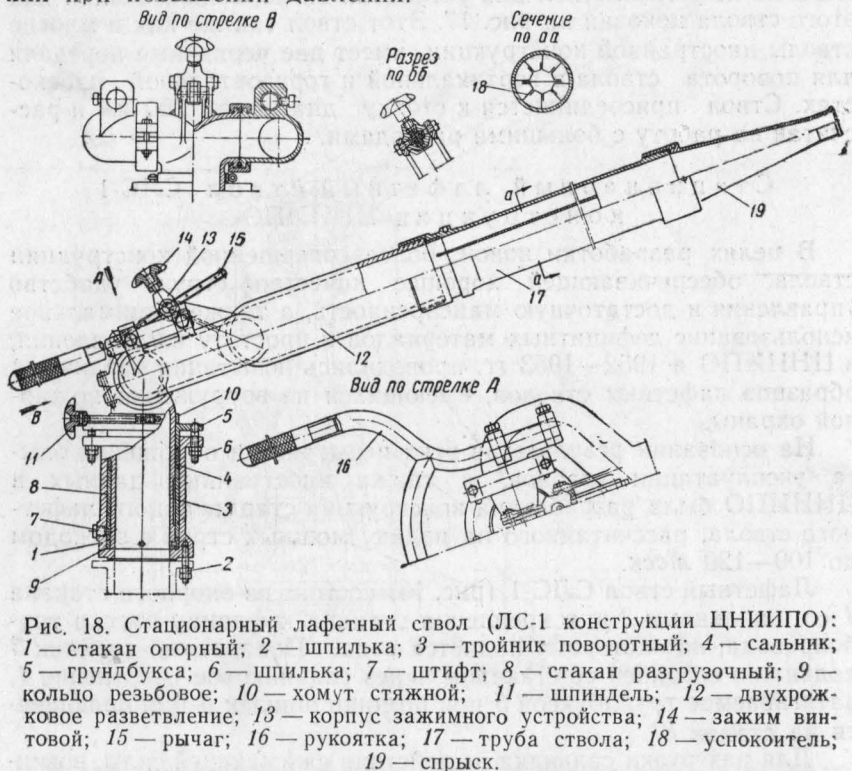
Стационарный лафетный ствол (ЛС-1 конструкции ЦНИИПО): 1 — стакан опорный; 2 — шпилька; 3 — тройник поворотный; 4 — сальник; 5 — грундбукса; 6 — шпилька; 7 — штифт; 8 — стакан разгрузочный; 9 — кольцо резьбовое; 10 — хомут стяжной; 11 — шпindel; 12 — двухрожковое разветвление; 13 — корпус зажимного устройства; 14 — зажим винтовой; 15 — рычаг; 16 — рукоятка; 17 — труба ствола; 18 — успокоитель; 19 — sprыск.
